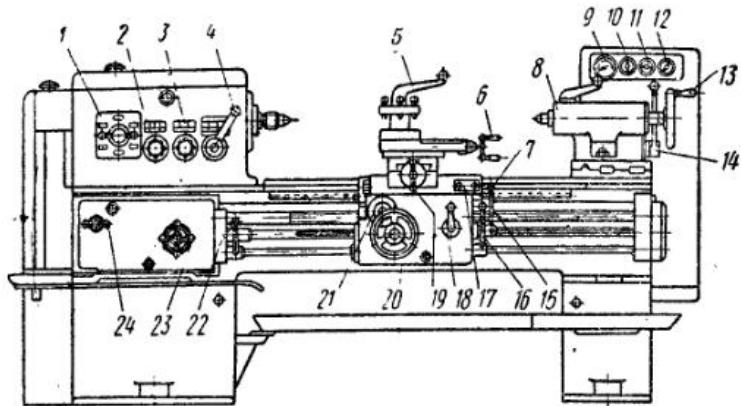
Органы управления токарно-винторезного станка 1К62:
